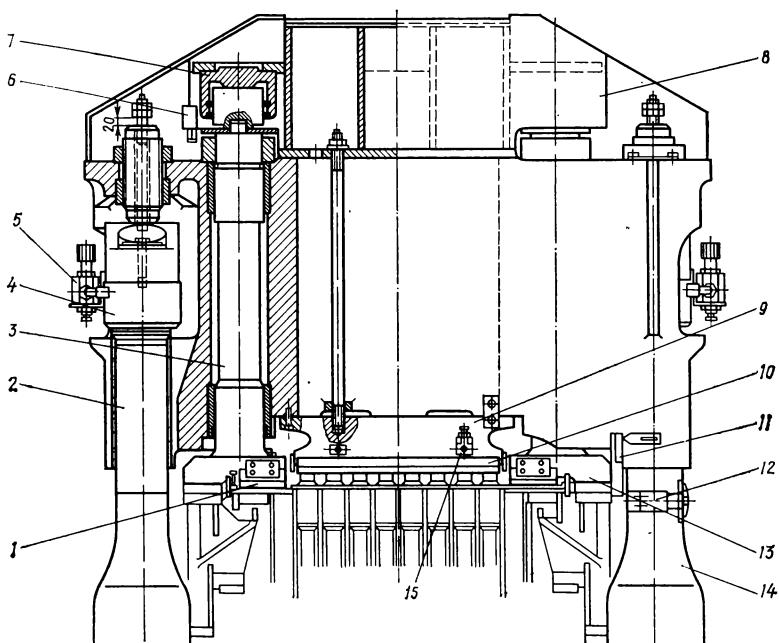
Устройство для верхней подпрессовки пресса-автомата РА-550:
